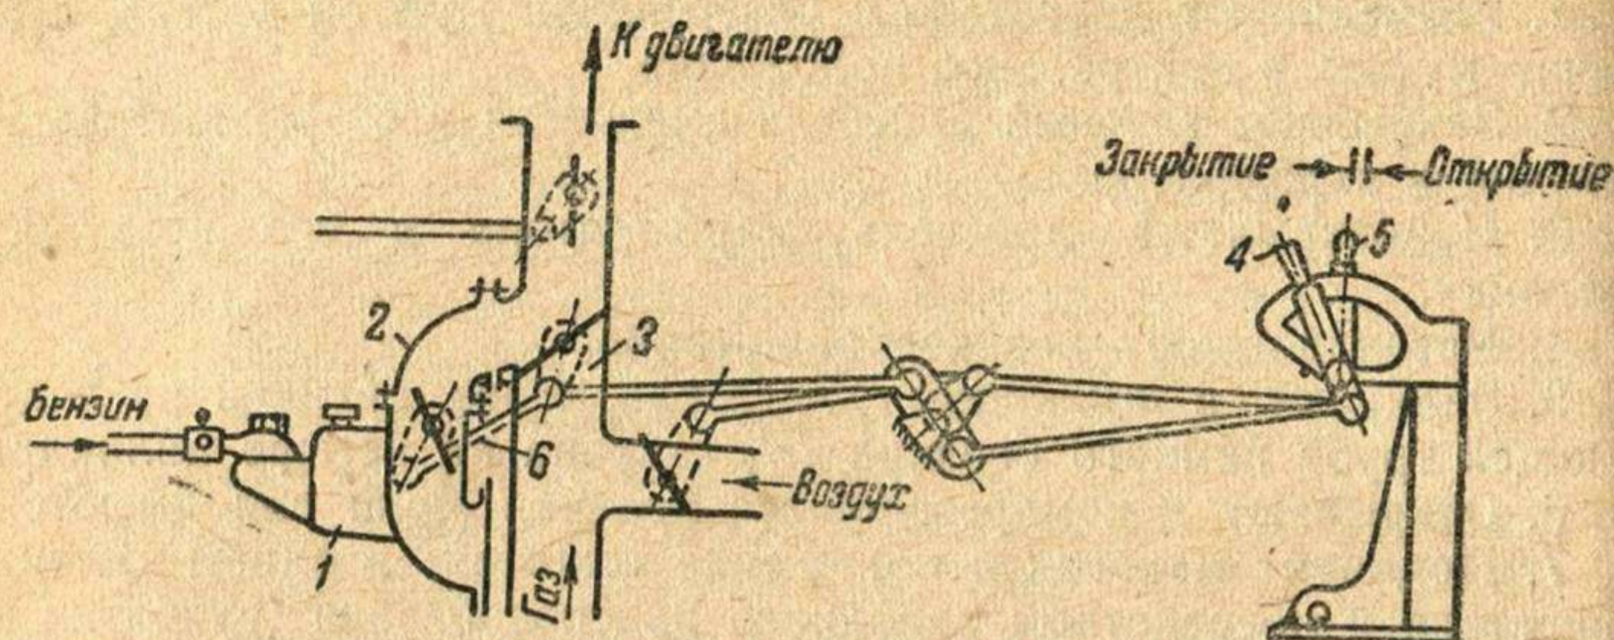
Схема рычагов управления питанием двигателя СГ-60:
